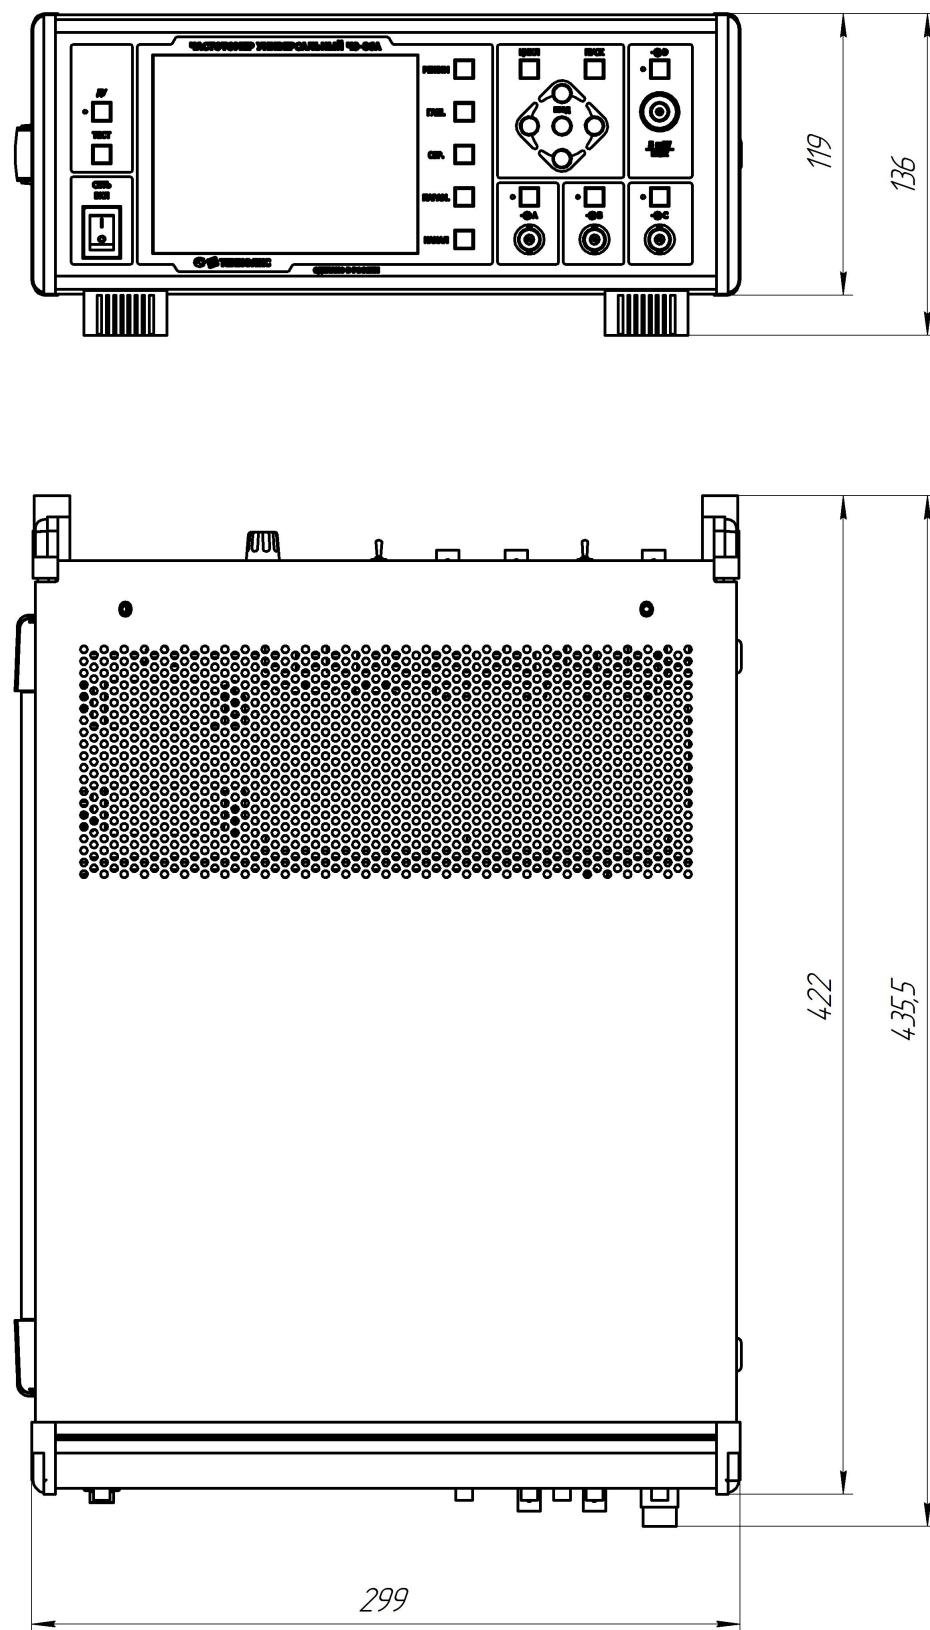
Габаритные размеры частотомера ЧЗ-86А
